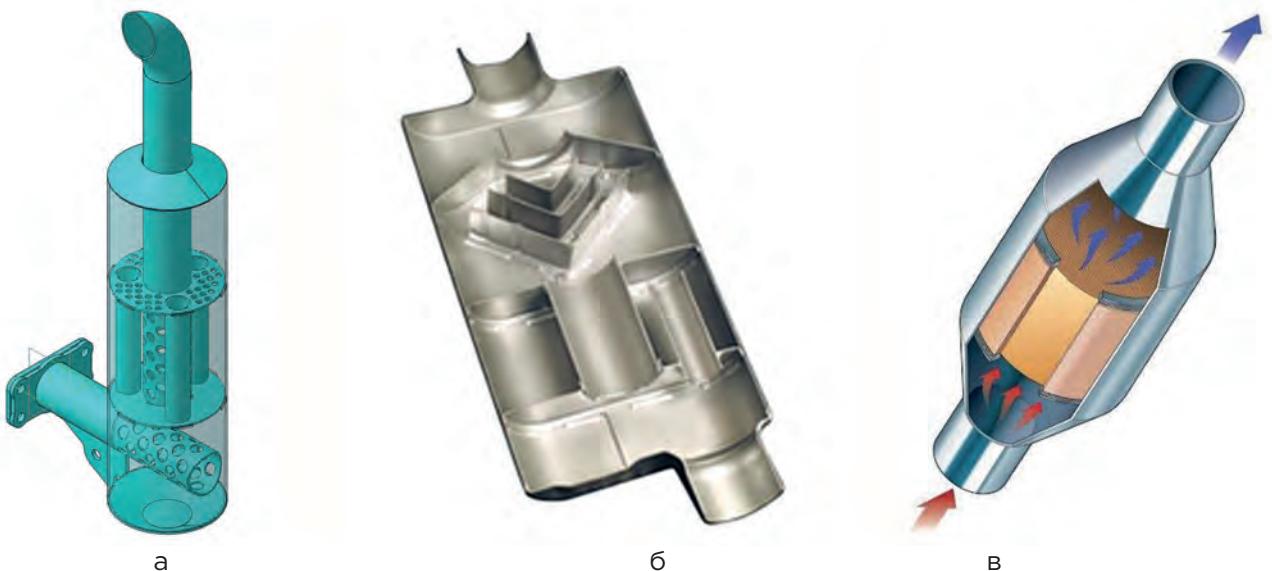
Основні види конструкцій глушників: а - глушник резонаторного типу; б - глушник лабіріントового типу; в - вставка-каталізатор
